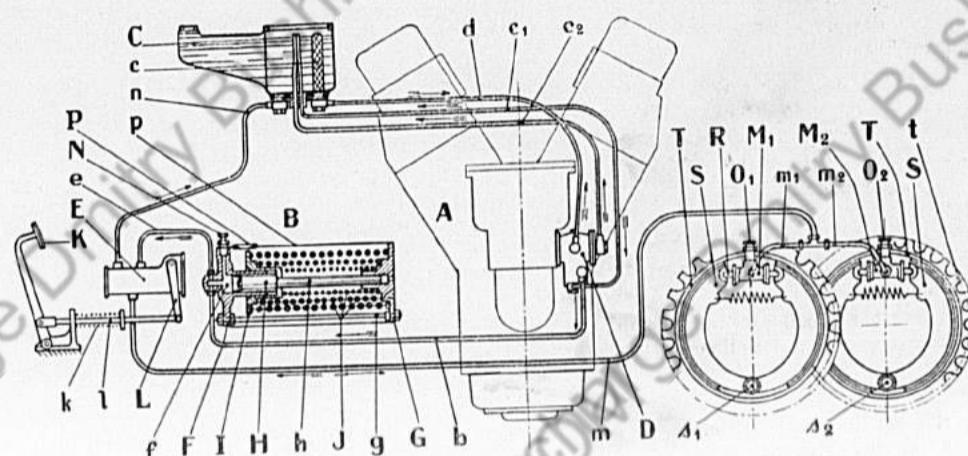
Fußbremse, auf die Triebräder der Gleisketten wirkend.
